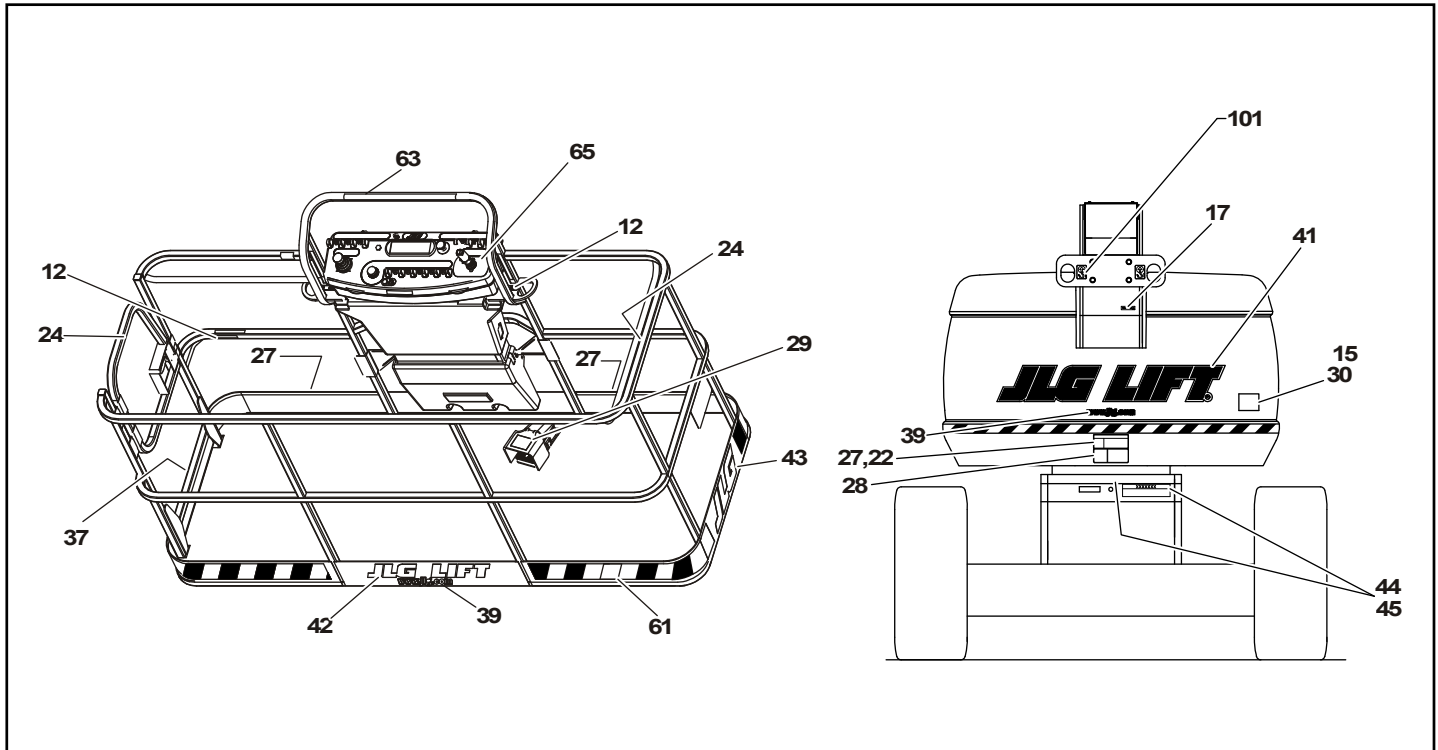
Placering av dekaler – Blad 4 av 4
